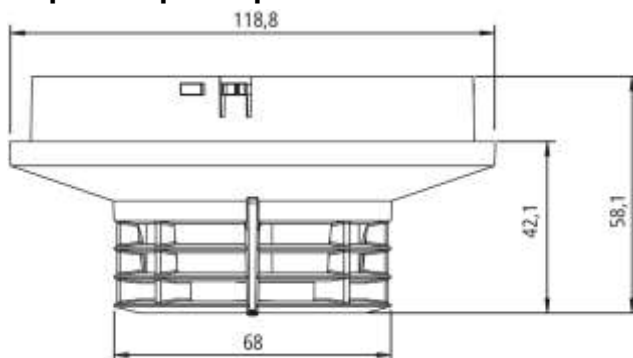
Чертеж детектора MMD 130 Ex-i с размерами
